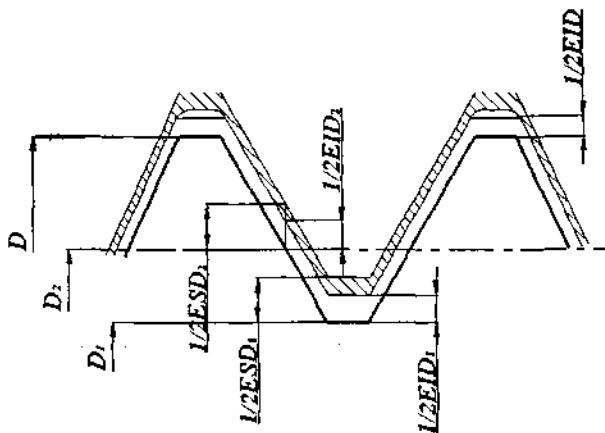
Схема расположения поля допуска гайки
